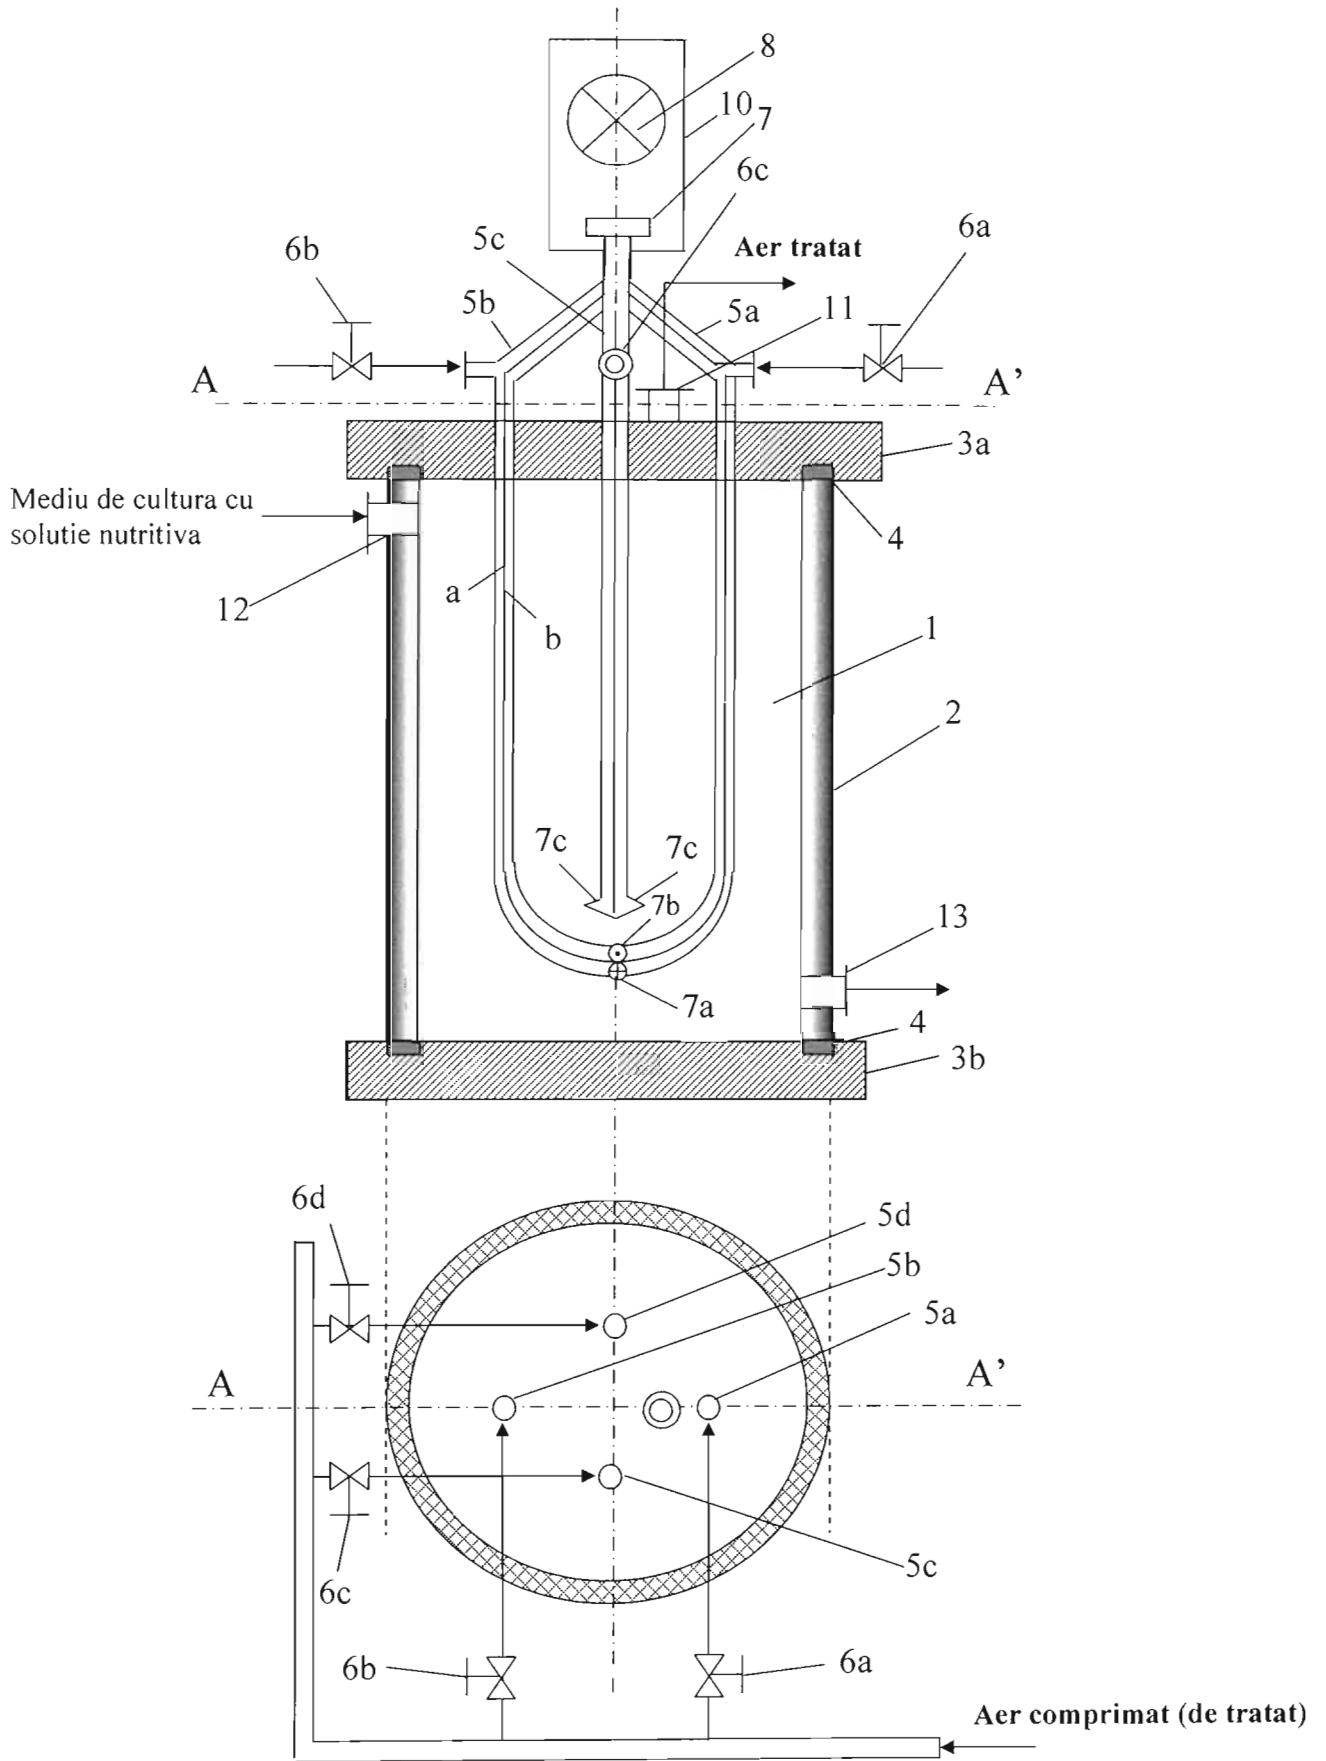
Fotobioreactor – elemente constructive in plan vertical si sectiune transversala
